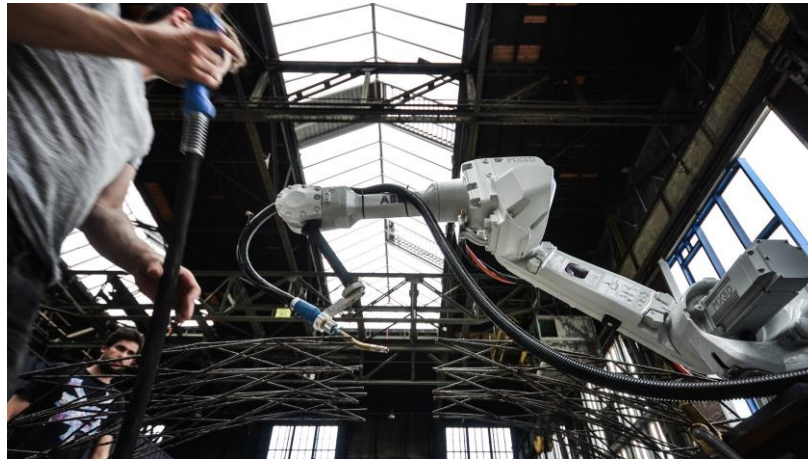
Máquina de impresión de MX3D. Fuente: <http://cort.as/-M7Fg>
